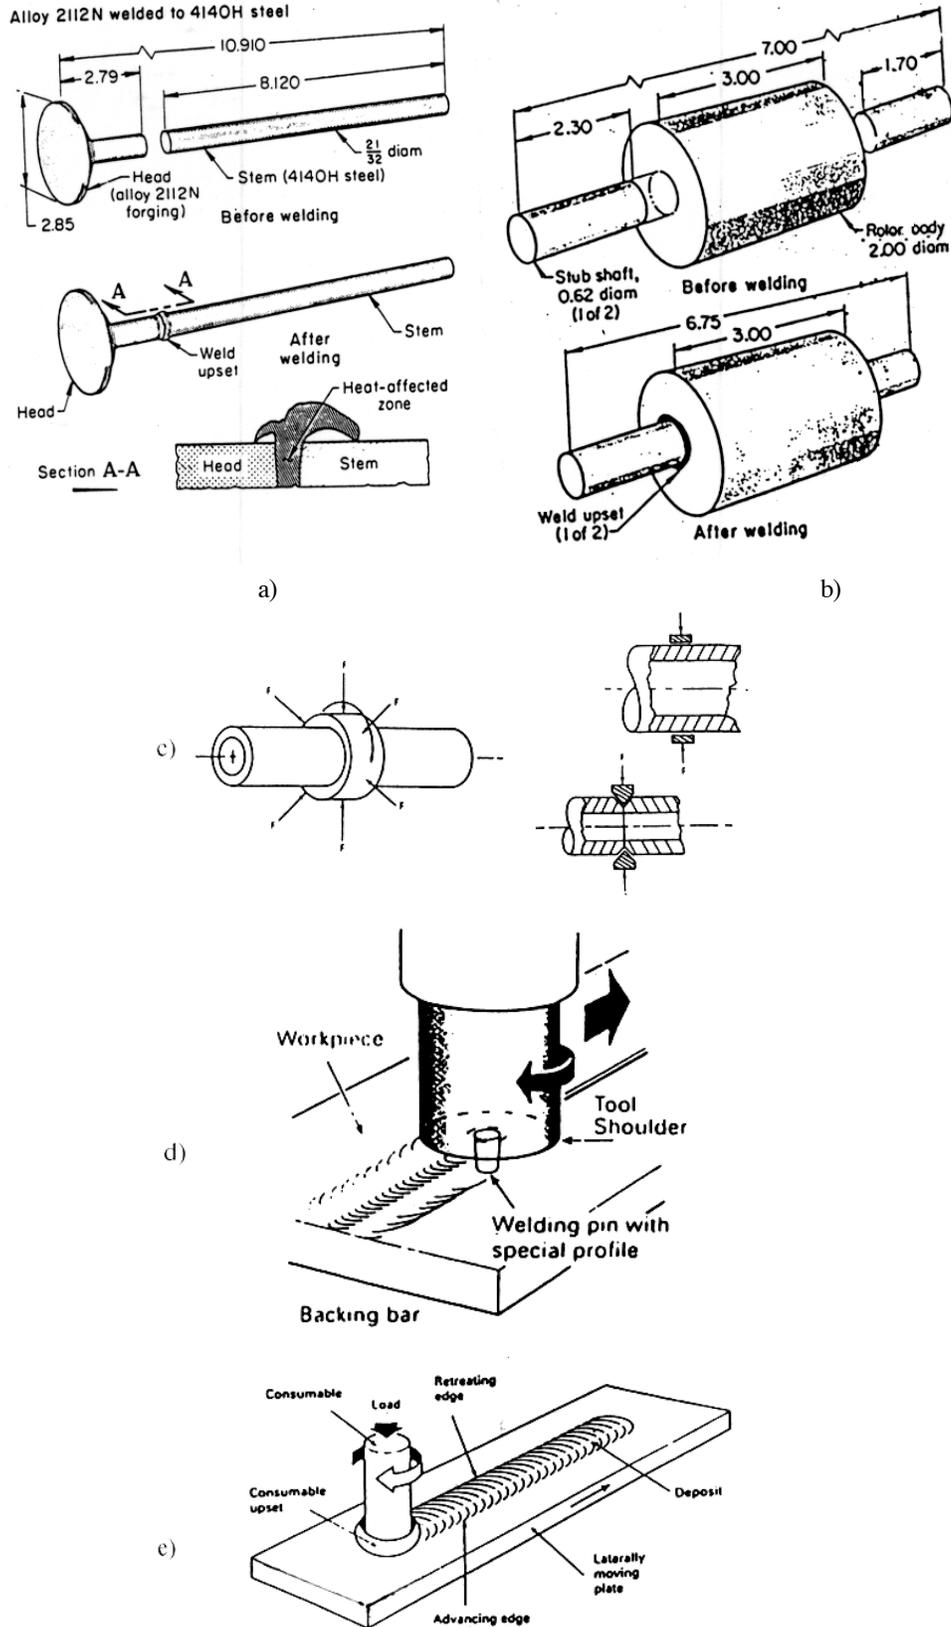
Différentes réalisations du soudage par friction: a) soudage d'un chapeau de soupape sur un piston de moindre qualité; b) soudage d'un arbre à diamètre variant; c) tuyaux joints par soudage par friction radiale; d) soudage bout à bout de deux tôles par friction stir welding; e) dépôt d'une couche de métal.
